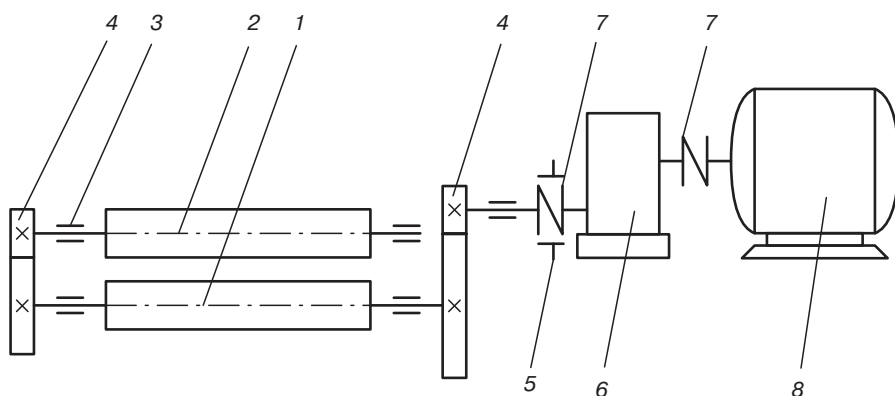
Кинематическая схема смесительных вальцов: 1, 2 — вальки; 3 — подшипники; 4 — открытые зубчатые пары; 5 — тормозное устройство; 6 — редуктор; 7 — муфта; 8 — электродвигатель
